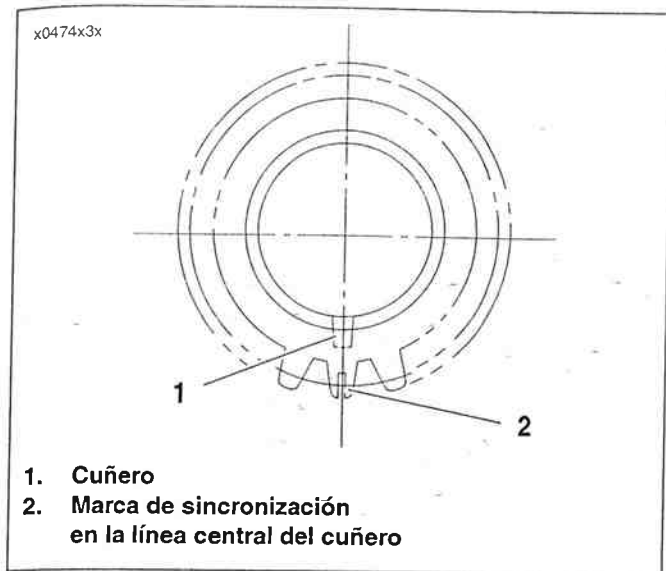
Marca de sincronización y cuñero del engranaje de piñón
